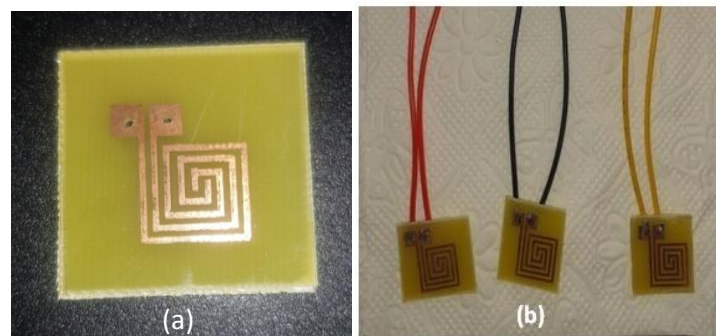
Dessin électronique forme spirale :(a) avant soudure, (b) après soudure
